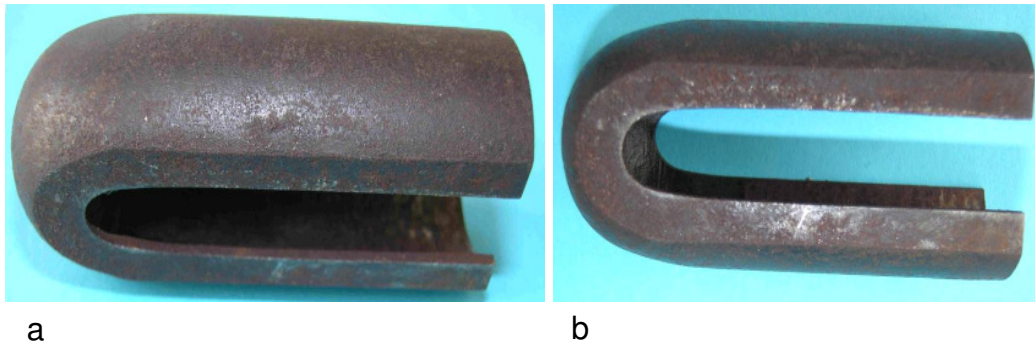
Zweipoliger Tulpenmagnet (Länge 75 mm, Magnetdicke 5mm): a) Sichtbare Außenfläche, b) Geschliffene Seiten des Magneten
